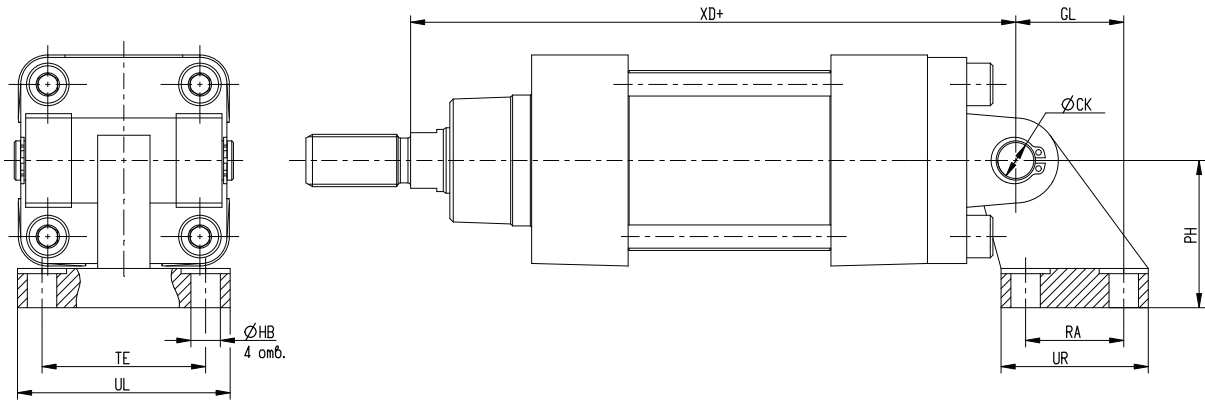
Пневмоцилиндр по стандарту ISO 15552
